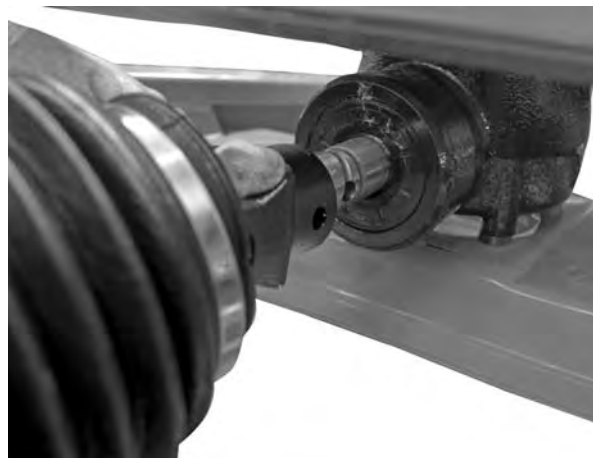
Gelenkwelle auf Getriebezapfen austecken
